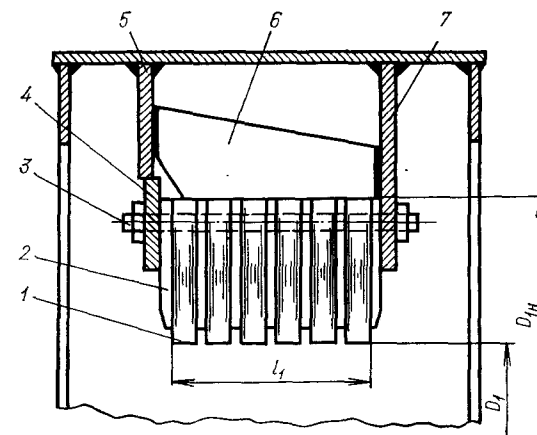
Крепление сердечника статора в сварной станине
